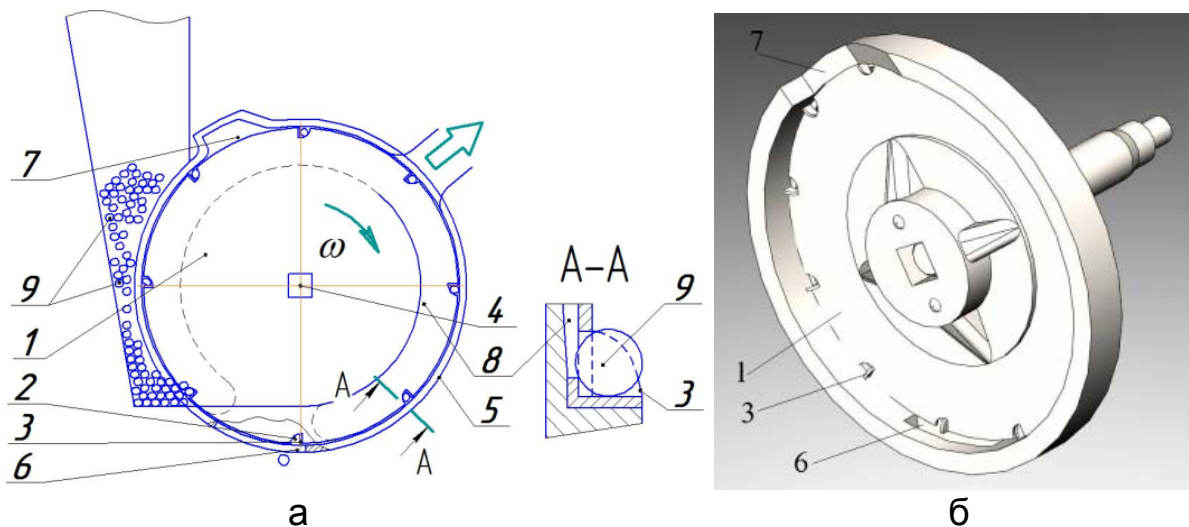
Пневмомеханічний висівний апарат: 1 – висівний диск; 2 – комірка; 3 – лопатка; 4 – приводний вал; 5 – корпус; 6 – висівне вікно; 7 – пасивний пристрій для видалення зайвого насіння; 8 – вакуумна камера; 9 – насіння; а – схема; б – трьохвимірна модель.
